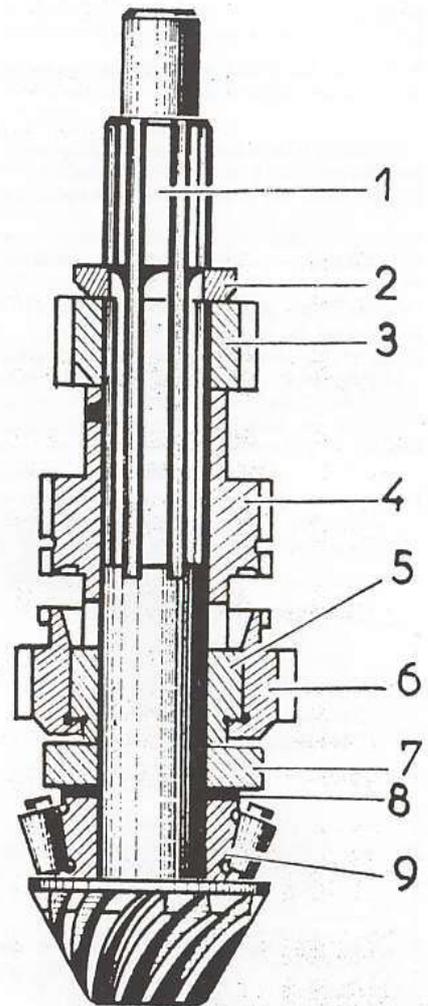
Vue en coupe des pièces empiéçées sur l'arbre pignon d'angle
